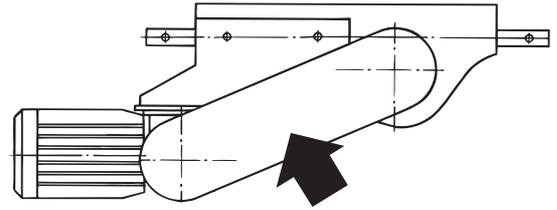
Защитный кожух для трансмиссии роликовой цепи
